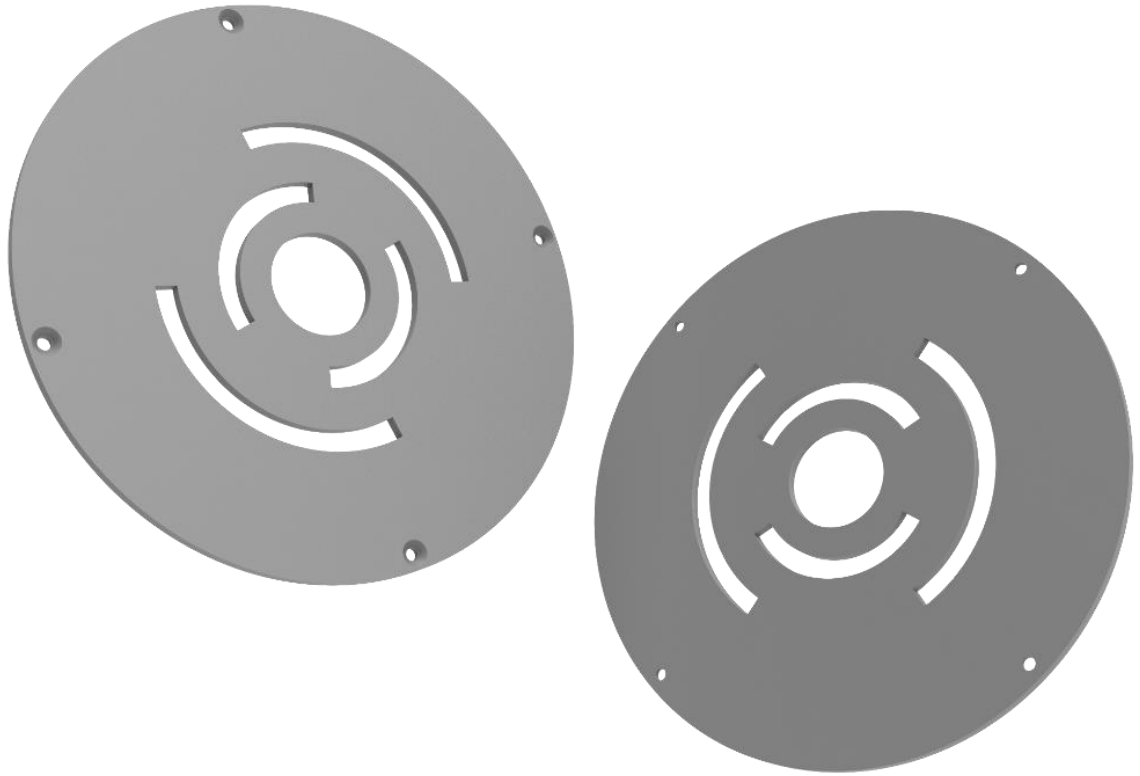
Vistas generales. Placa superior sin ensamblaje.
